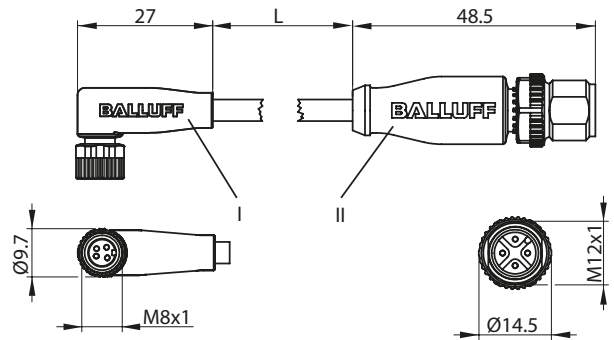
Steckverbinder Buchse gewinkelt – Stecker gerade
